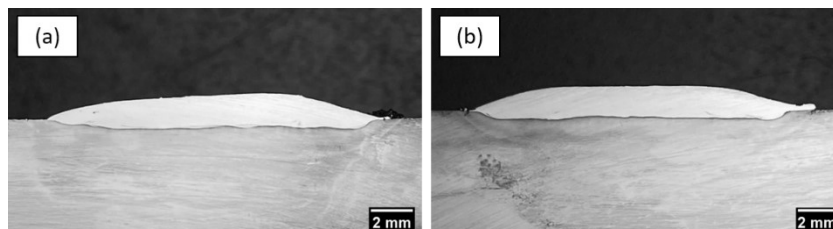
Aspecto superficial dos cordões de solda obtidos com tecimento e deposição do Stellite 1 sobre aço AISI H13 com corrente de soldagem de (a) 130 A (TS13013) e (b) 140 A (TS14013)
